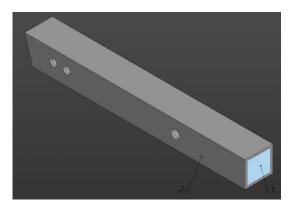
Модель композитной детали: 1 — металлополимерный заполнитель; 2 — пустотелая оболочка
